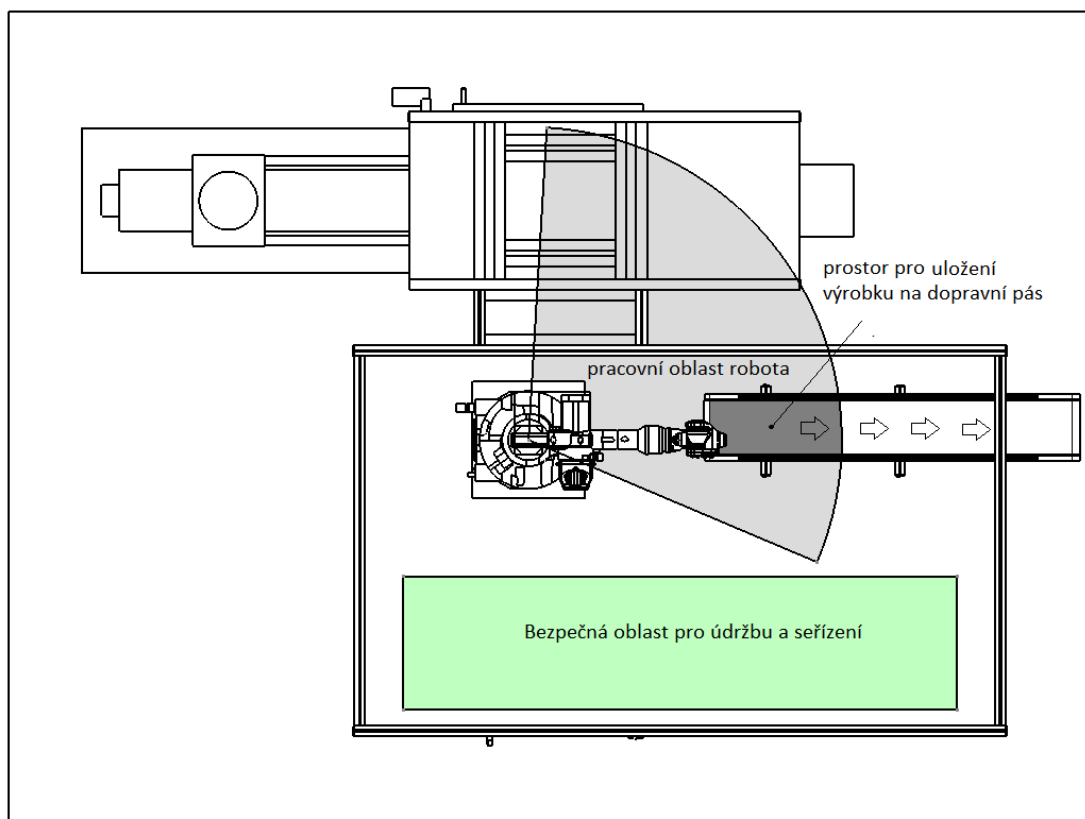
Manipulační robot typ R 16-2 CR [22]
